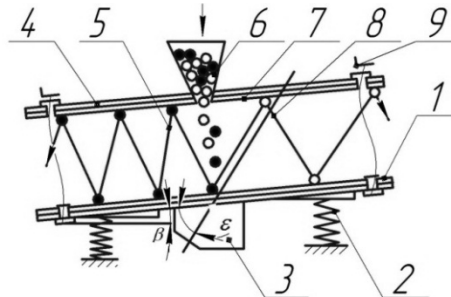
Схема сепаратора з відбивною робочою поверхнею: 1 – робоча поверхня; 2 – пружина; 3 – вібробудник; 4 – відбивна поверхня; 5 – траєкторія руху округлого, гладкого насіння; 6 – живильний пристрій; 7 – фрикційний матеріал; 8 – траєкторія руху плоского, шорсткуватого насіння та домішок; 9 – гвинтовий регулювальний пристрій
